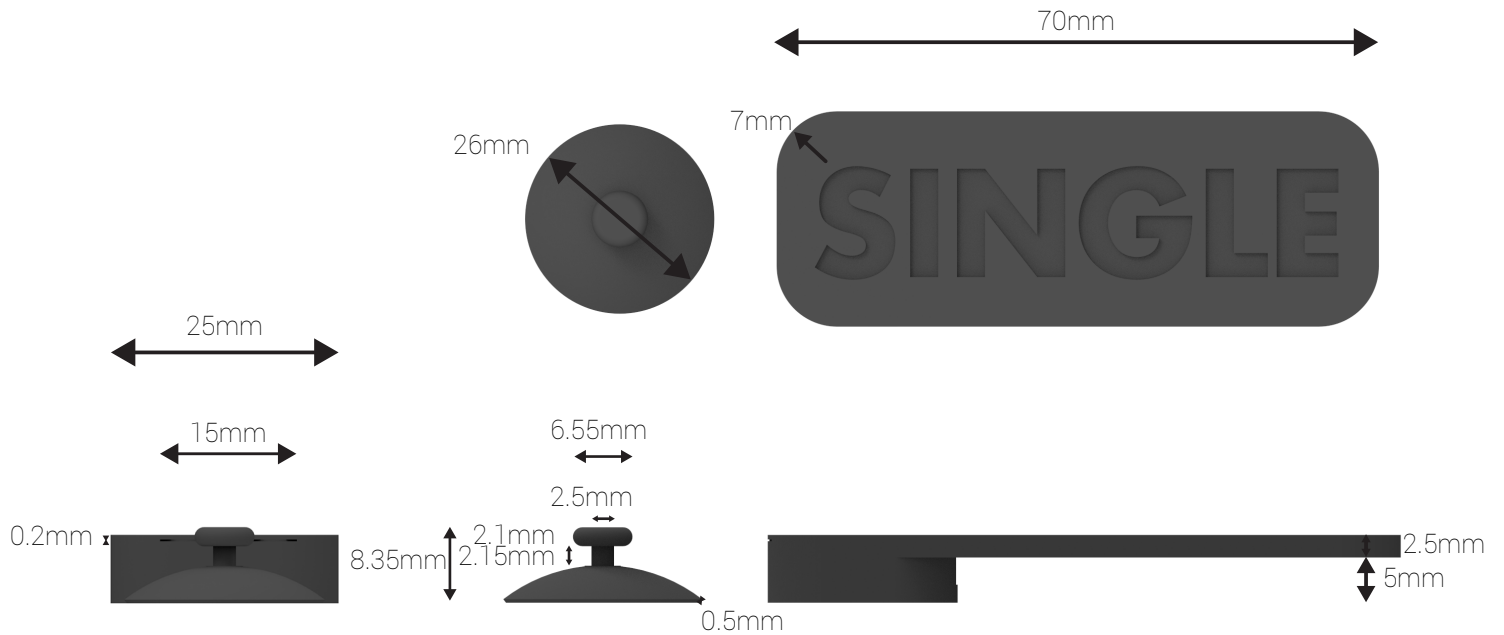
Planos de construcción de la propuesta para envases. Elaboración propia
